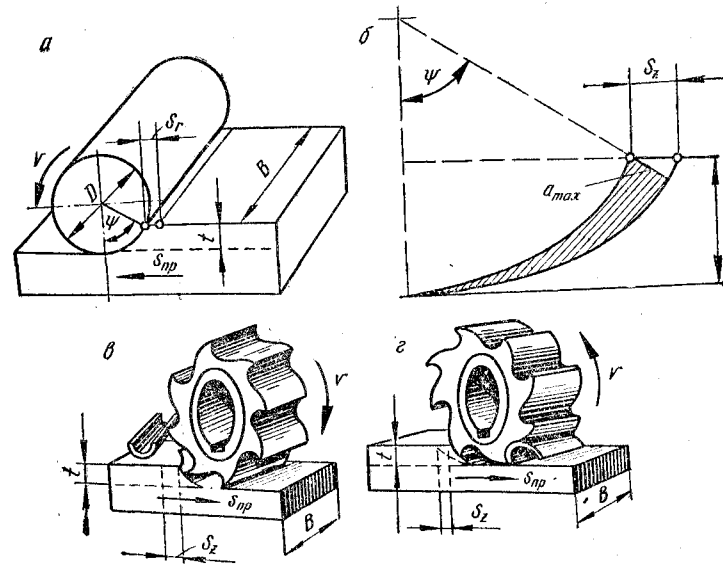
Схема работы цилиндрической фрезы и элементы резания
